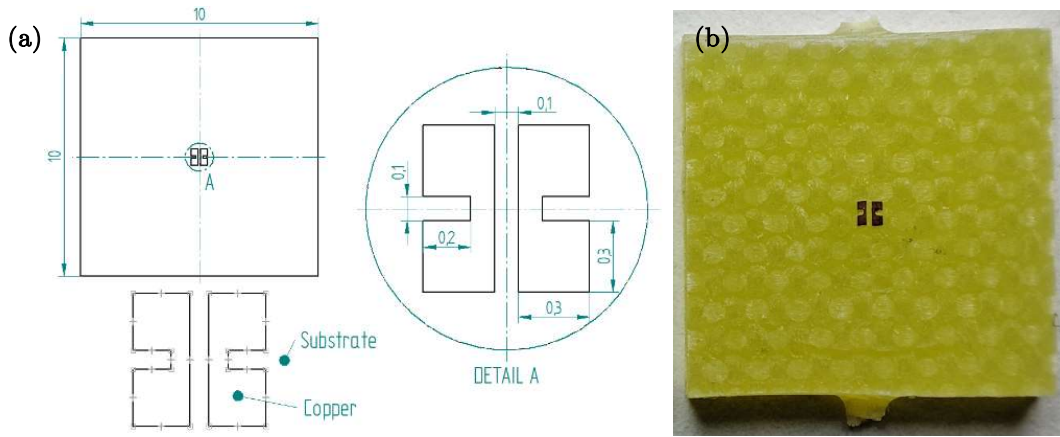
Plano de la PCB auxiliar (a) y PCB fabricada por microfresado (b).
